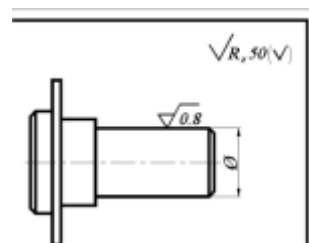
Обозначения шероховатости, одинаковой для части поверхности
